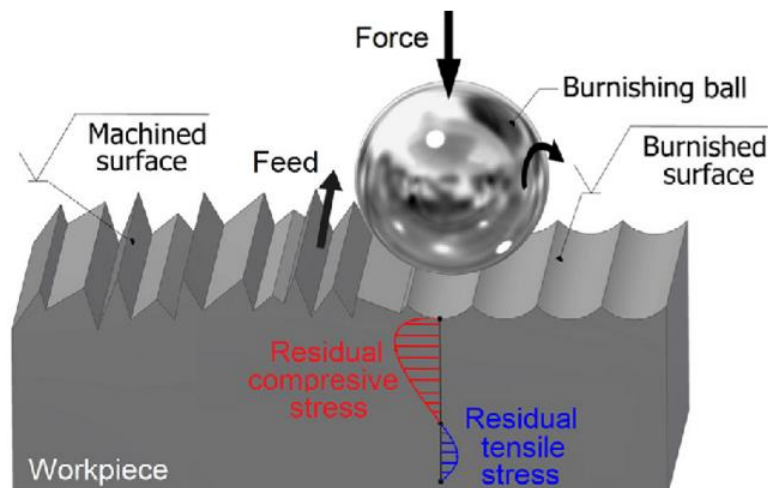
Схема процесу вигладжування поверхні кулькою [16]
